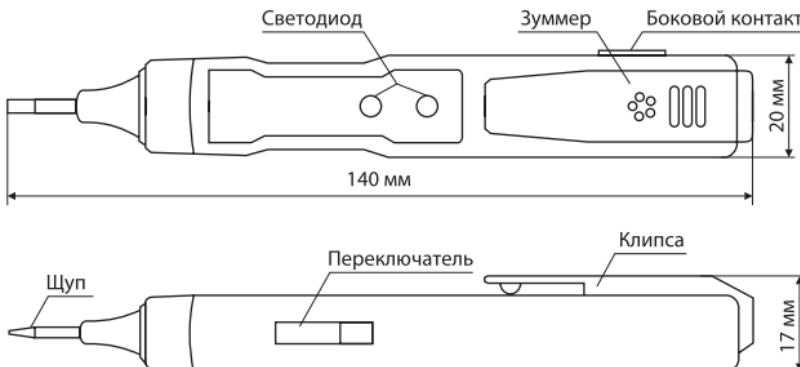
Габаритные размеры и основные элементы отвертки-пробника ОП-2Э
